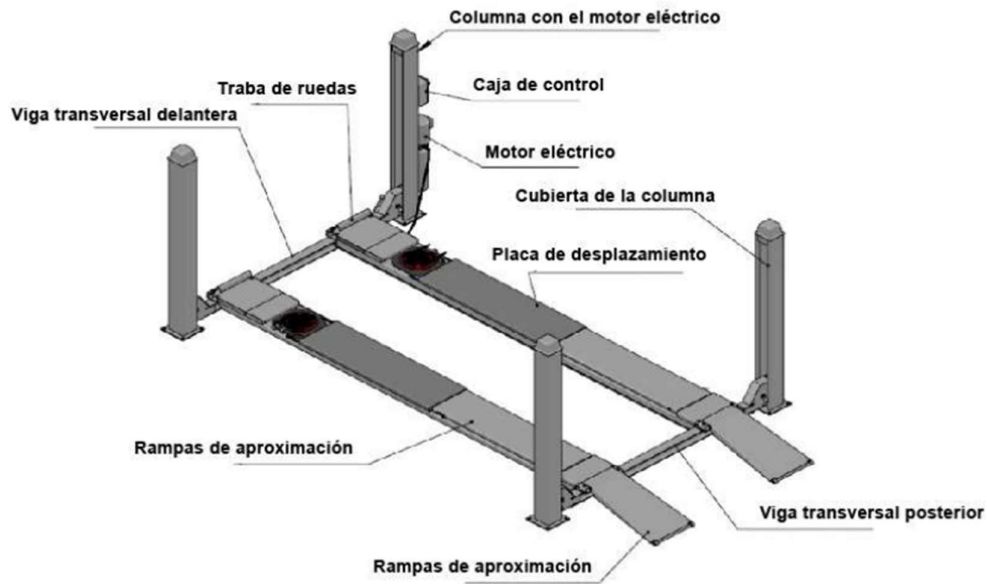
Descripción de partes Elevador cuatro columnas ALM.
